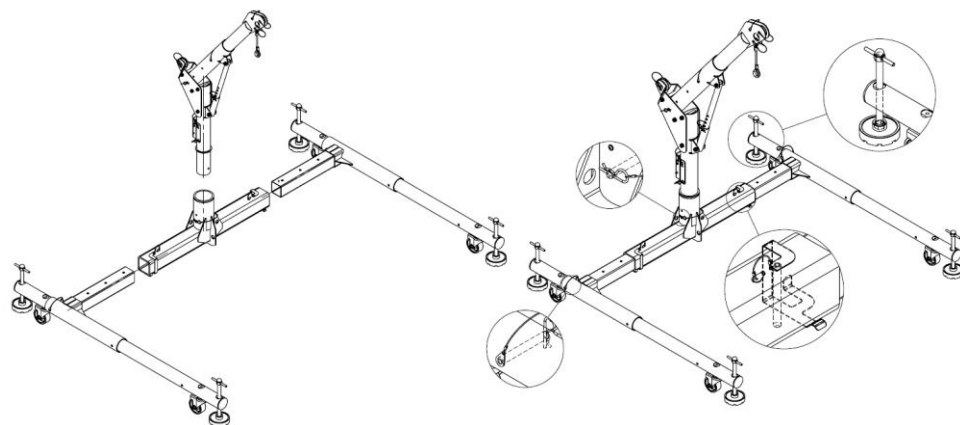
Монтаж СОБ Кран Е11-1L
